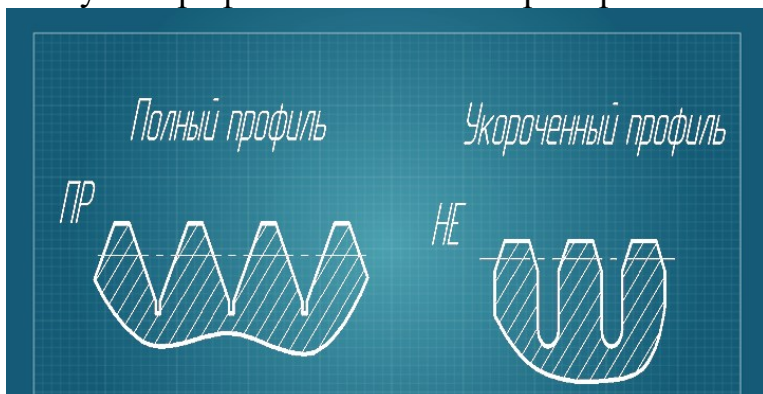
Проходимый и непроходимый резьбовой калибр
